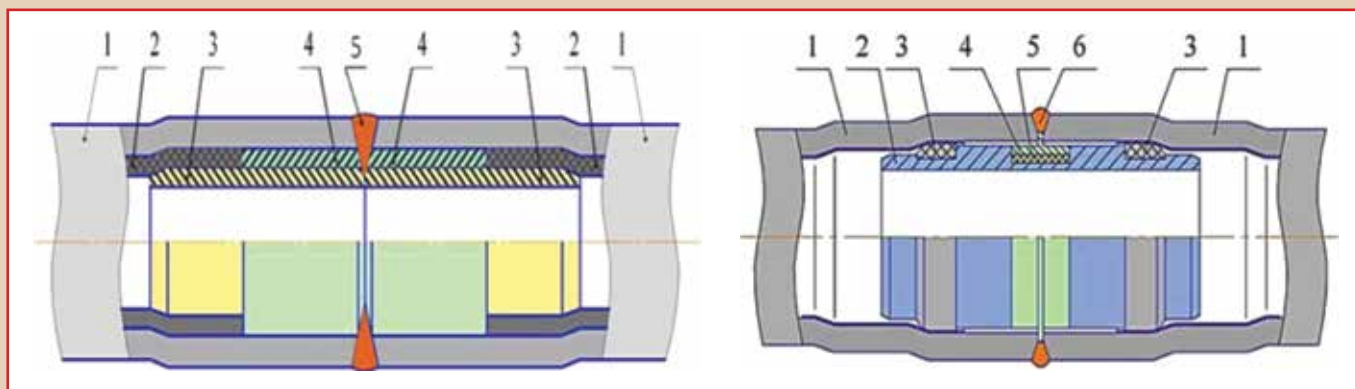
Конструкции околошовной зоны полевого сварочного стыка металлопластмассовых труб (а) и труб с полимерным внутренним покрытием (б)
